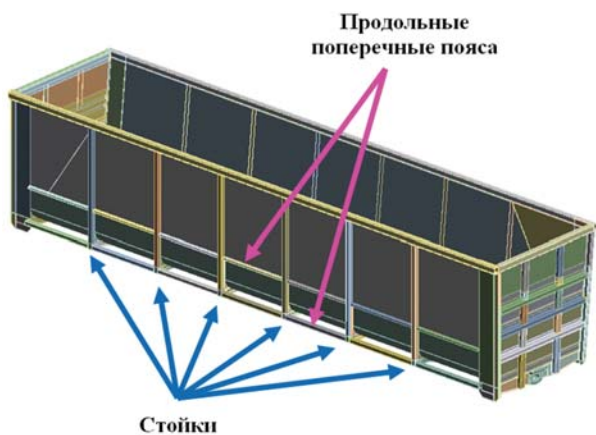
Стойки постоянного по высоте сечения, соединенные двумя продольными поперечными поясами
